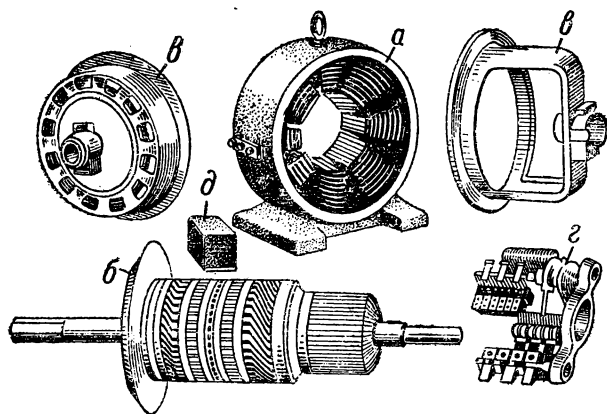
Генератор постоянного тока в разобранном виде: а — станина; б — якорь; в — подшипниковые шиты; г — щетки с щеткодержателями, укрепленные на так называемой траверзе; д — сердечник полюса.
